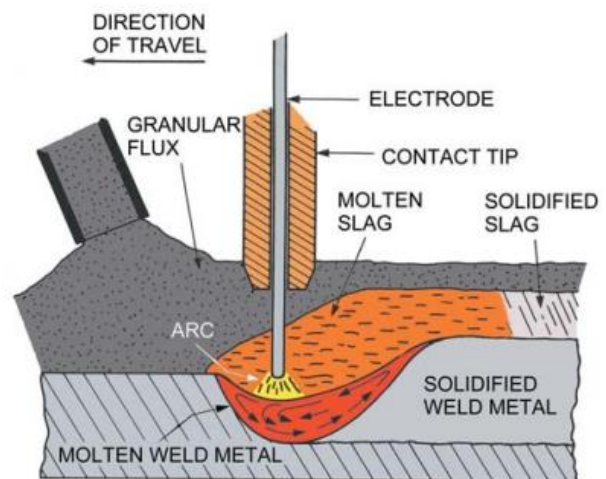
Processo de soldadura com arco submerso [3B]
